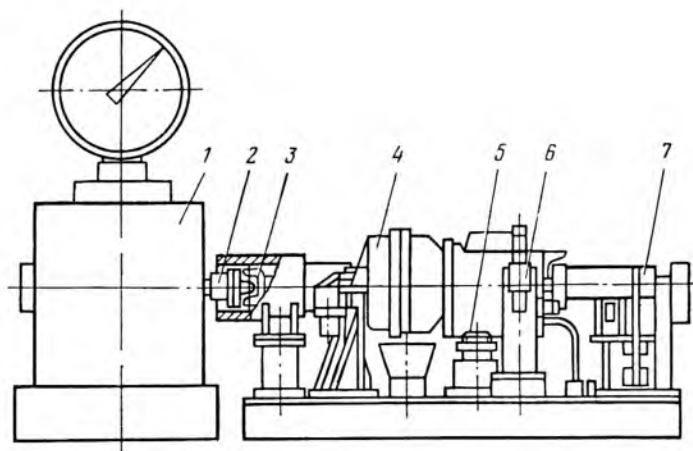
Стенд для обкатки гидромеханической передачи без нагрузки:
